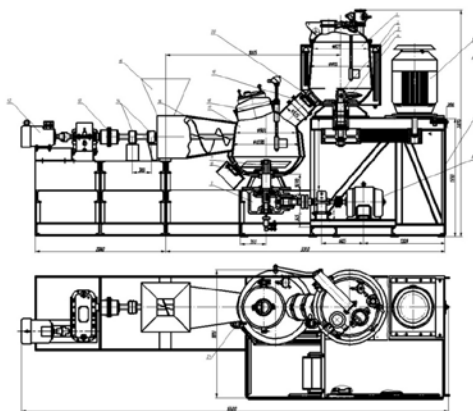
Двухкамерный высокотемпературный вакуум смеситель:
